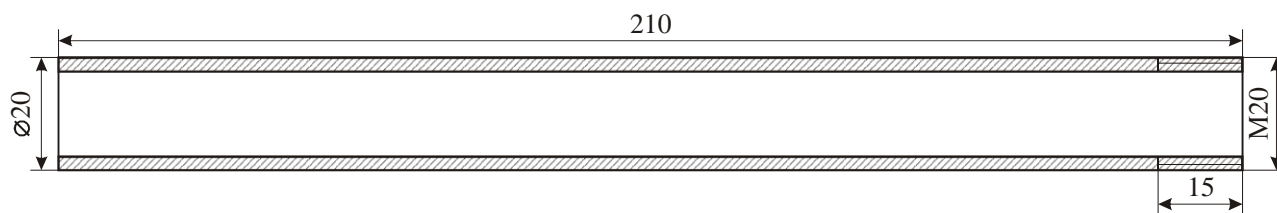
Эскиз заготовки для капсулы после нарезания резьбы
